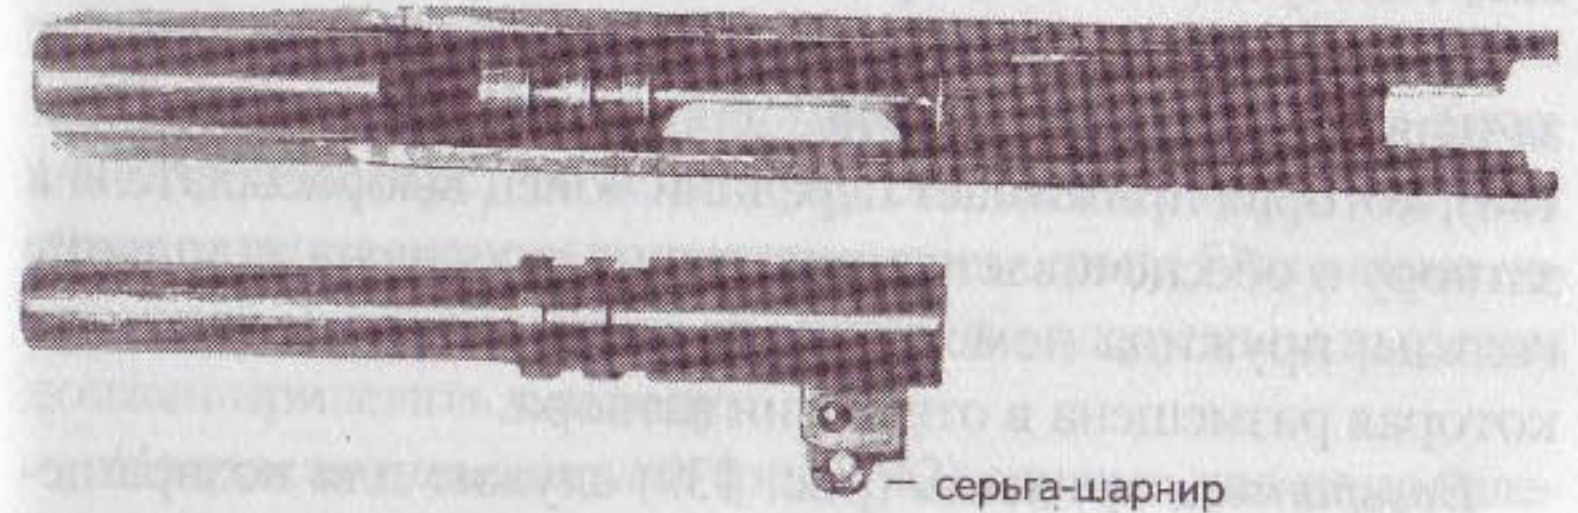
Затвор с внутренней стороны и ствол: на рисунке видны опорные выступы на внутренней поверхности кожуха-затвора и кольцевые выточки на казенной части ствола, которыми эти две детали сцепляются друг с другом при выстреле
